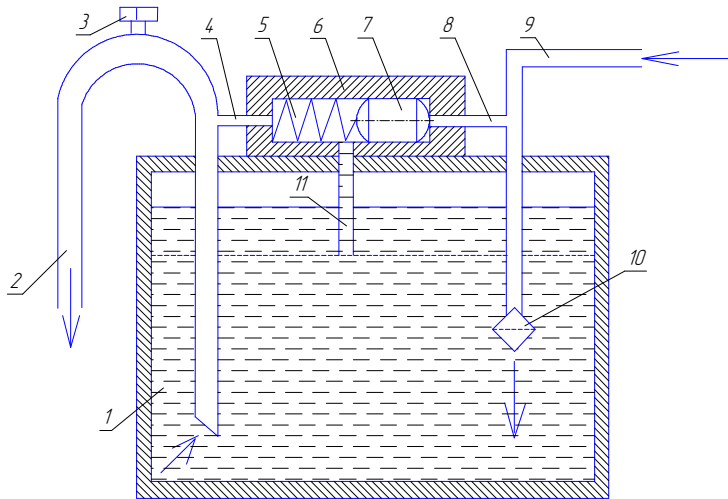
Гідробак з системою аварійного захисту гідросистеми: 1 – гідробак; 2 – відбірна труба; 3 – пробка; 4, 8 – з'єднувальні канали; 5 – пружина; 6 – корпус; 7 – клапан; 9 – зливна труба; 10 – фільтр; 11 – додаткова відбірна труба
